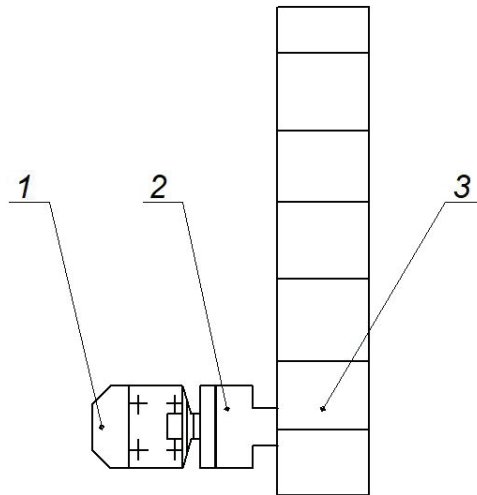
Схема привода установки: 1 — Мотор-редуктор; 2 — Вал с муфтой; 3 — Лента
